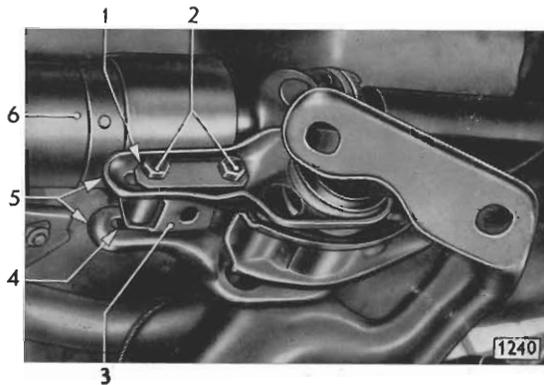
Anschlußstücke des Hinterachsgelenkes am Halter des Stützrohres befestigt
